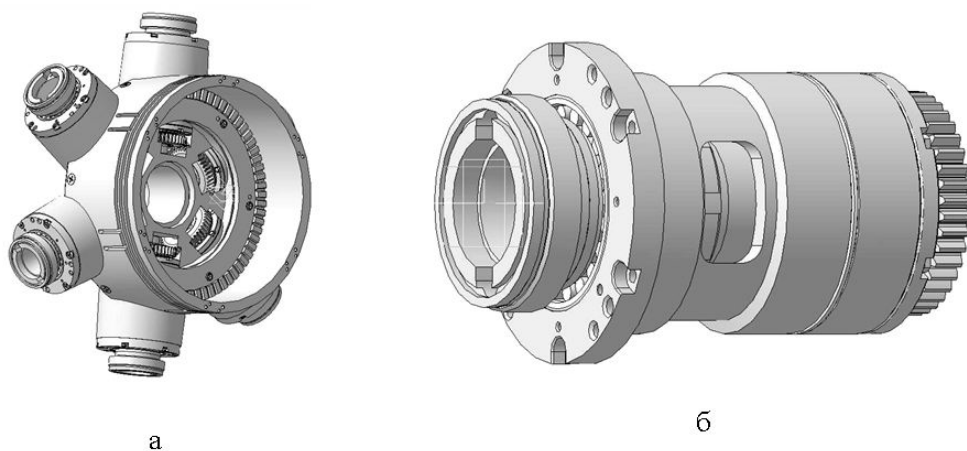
3D-модели формообразующих узлов: а – шестишпиндельная револьверная головка; б – шпиндельный узел
